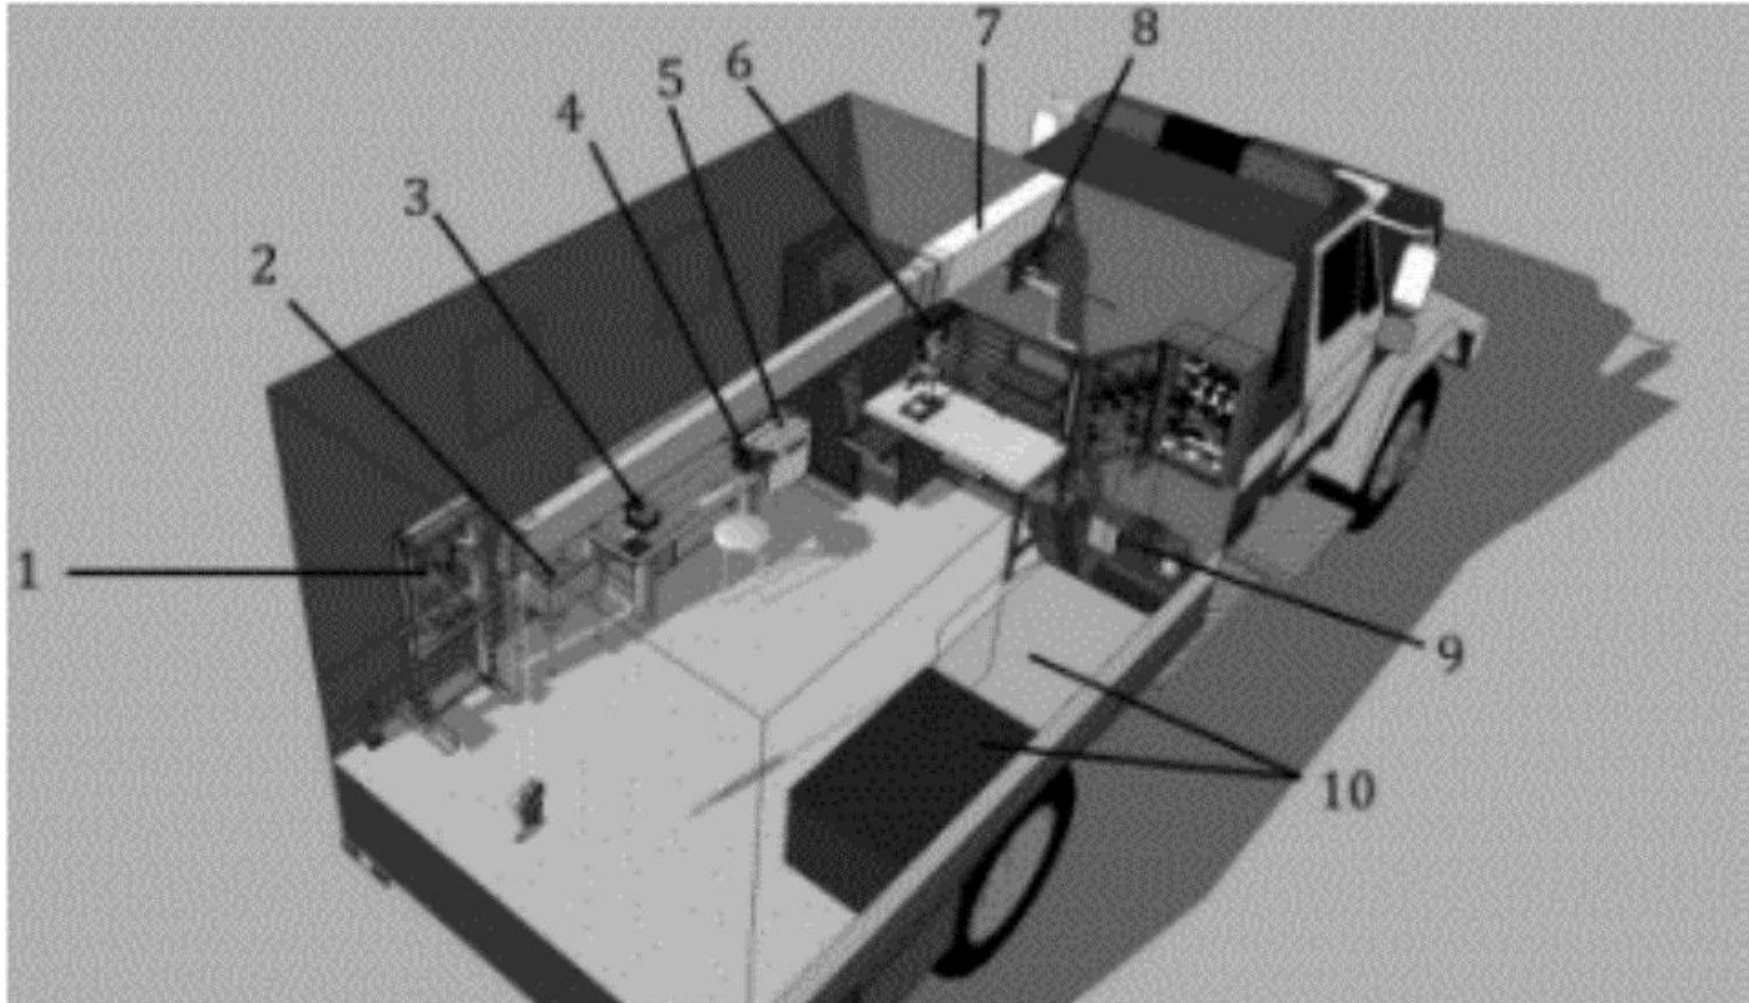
Модель рабочего пространства с расположением оборудования передвижной мастерской: 1 – пресс гидравлический, 2 – мойка, 3 – станок заточной, 4 – тиски, 5 – сварочный аппарат, 6 – сверлильный станок, 7 – грузовая стрела, 8 – редуктор, 9 – компрессор, 10 – рундук
